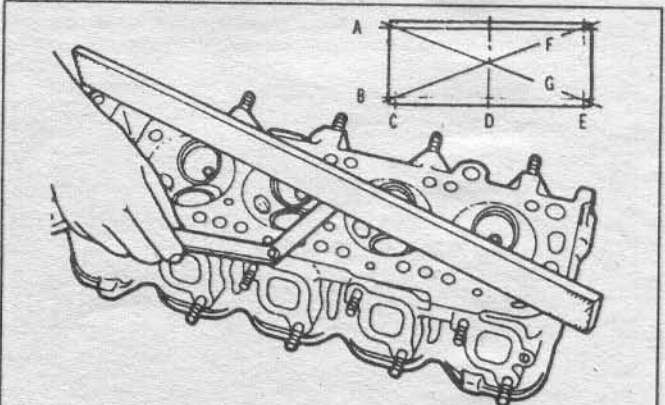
Контроль коробления головки с помощью плоскопараллельного бруса и щупа.
